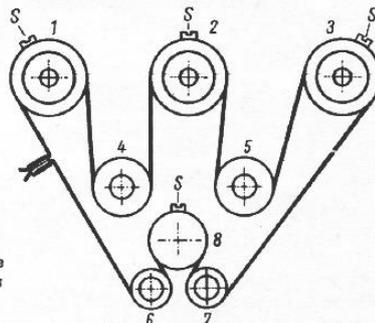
Skizze des Seiltriebes und dessen Einzelteile
